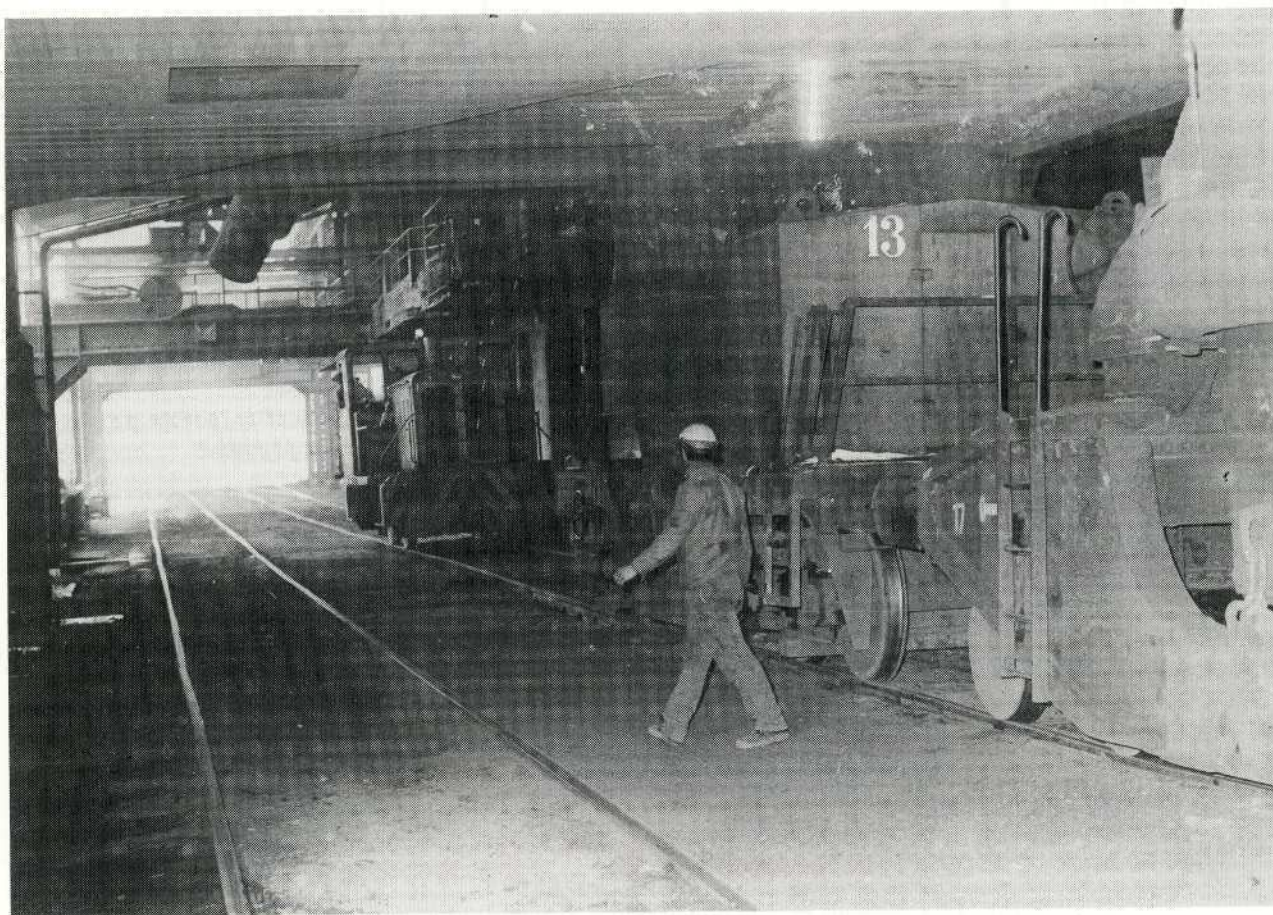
Tunnel de coulée de la fonte et du laitier situé sous le plancher du haut-fourneau.
